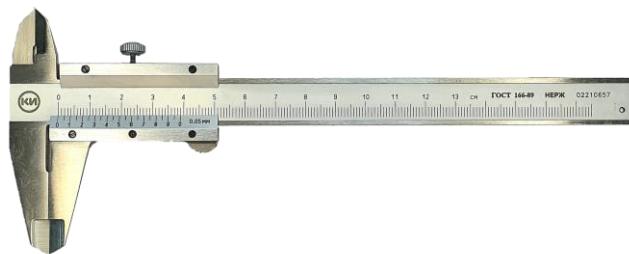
Общий вид штангенциркулей ШЦ-І
